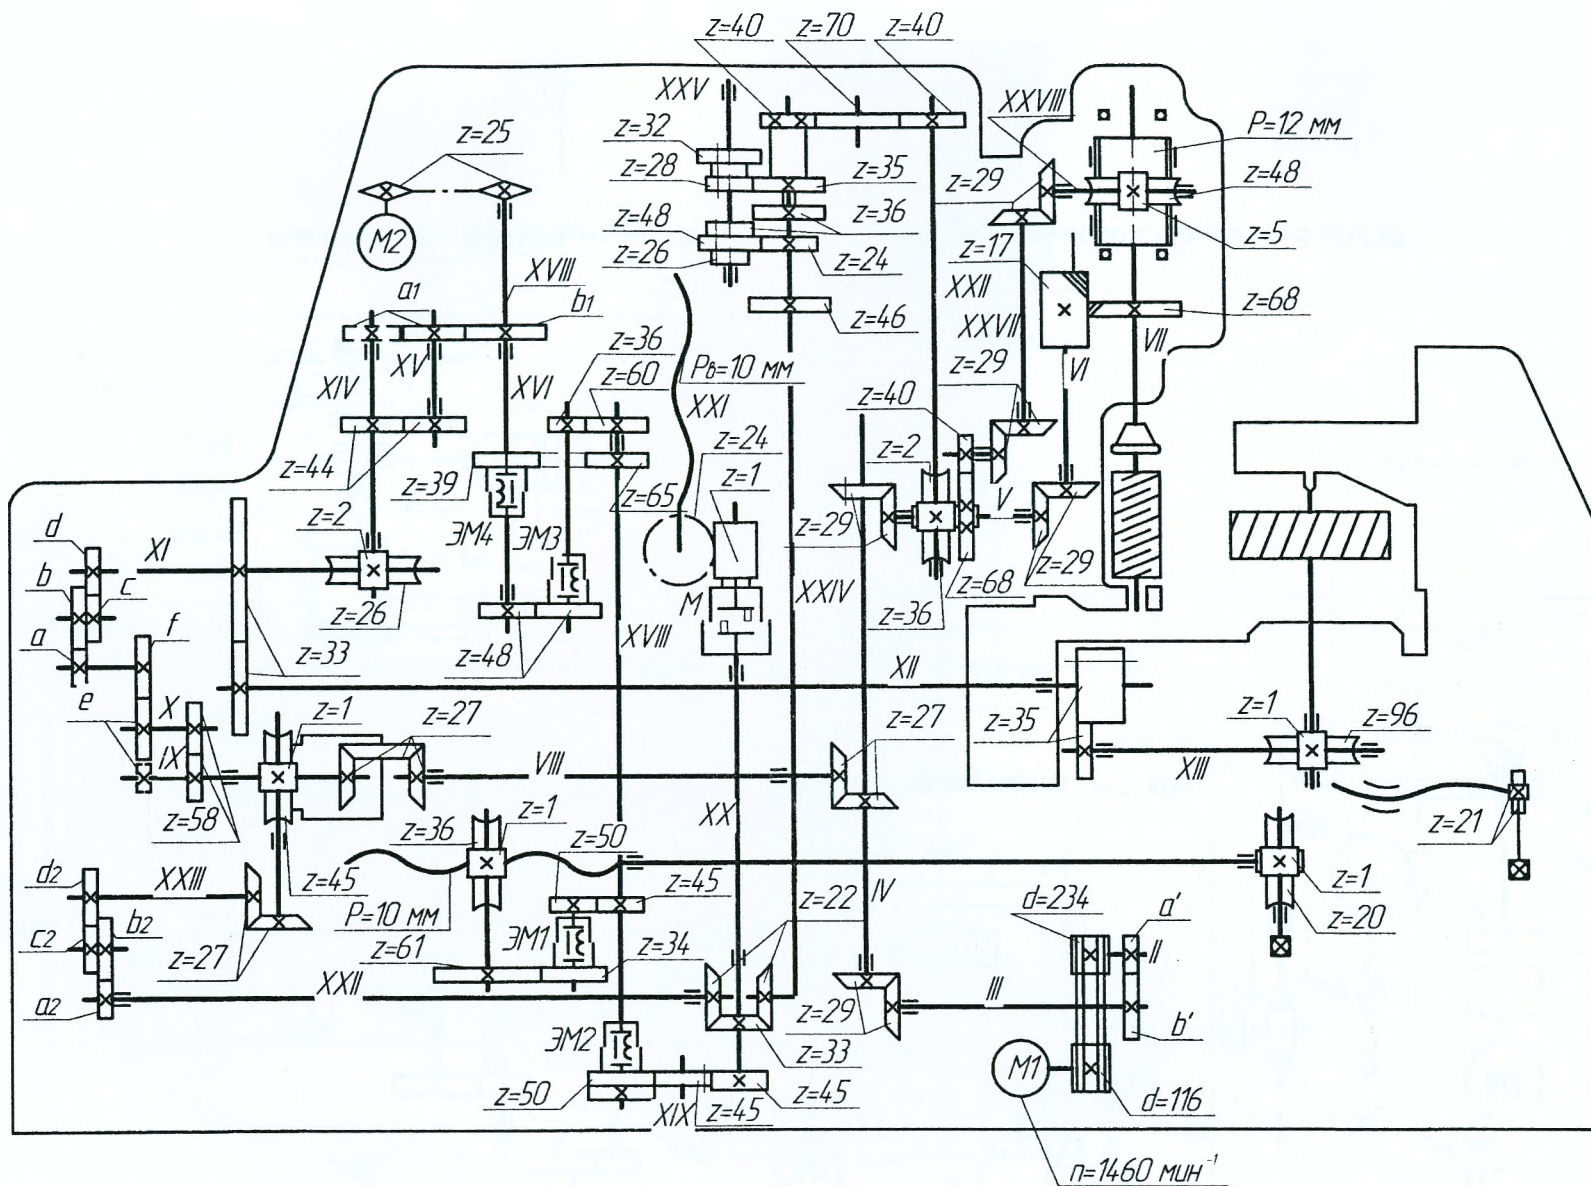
Кинематическая схема зубофрезерного станка мод.5K32
